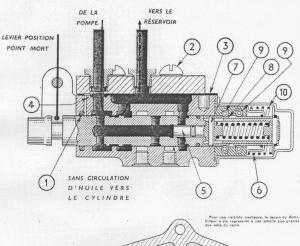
ENSEMBLE DU DISTRIBUTEUR MONTÉ
